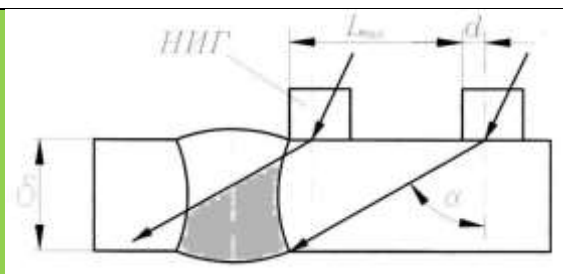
Контроль сварного соединения прямым лучом
